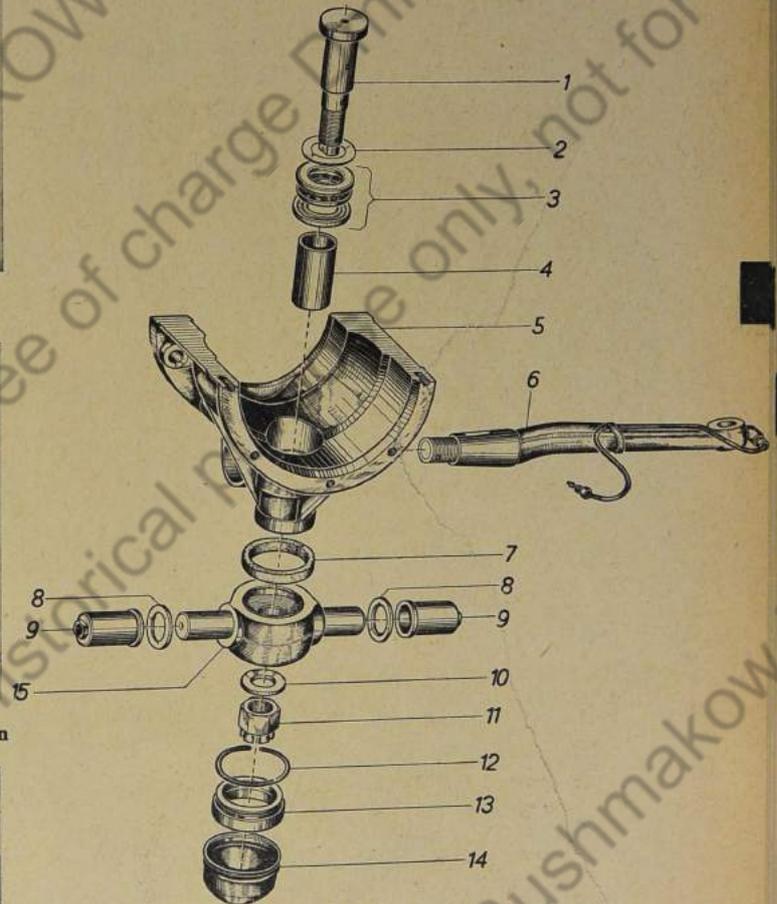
Unterer Lagerzapfen und Achsbolzen-Zusammenbau
